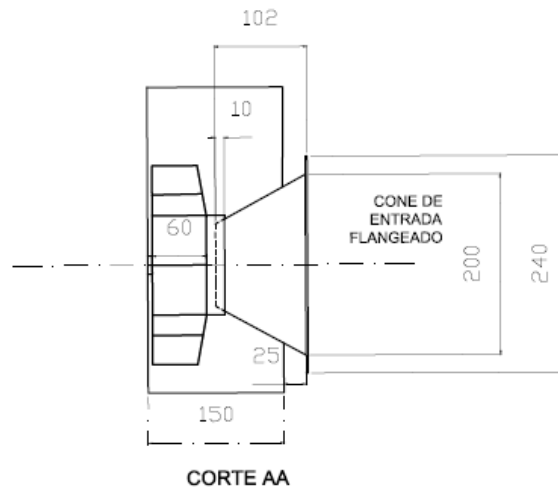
Rotor e bocal do sistema de exaustão e compressão.
